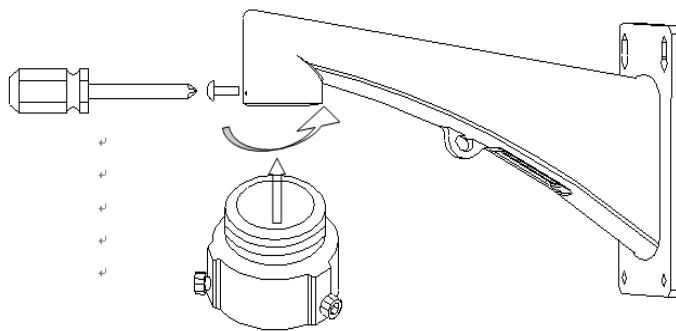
2 Anbringen des Schnellmontageadapters
